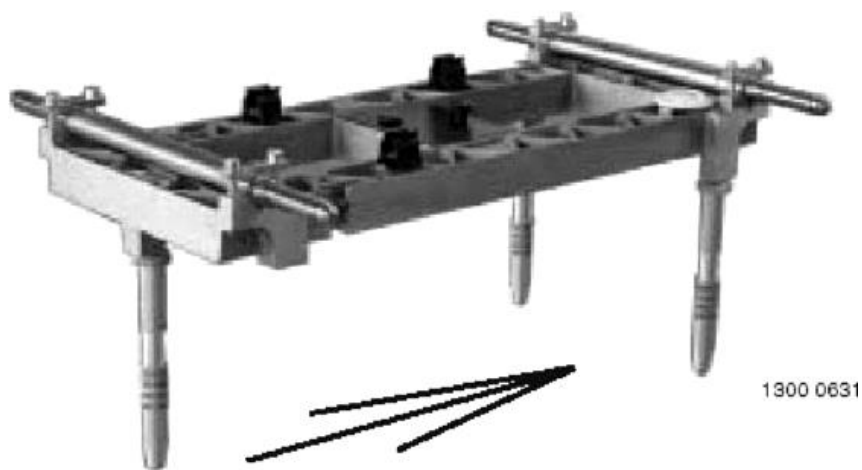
Конструкція пристрою для калібрування головок CCD-стенда [8]
